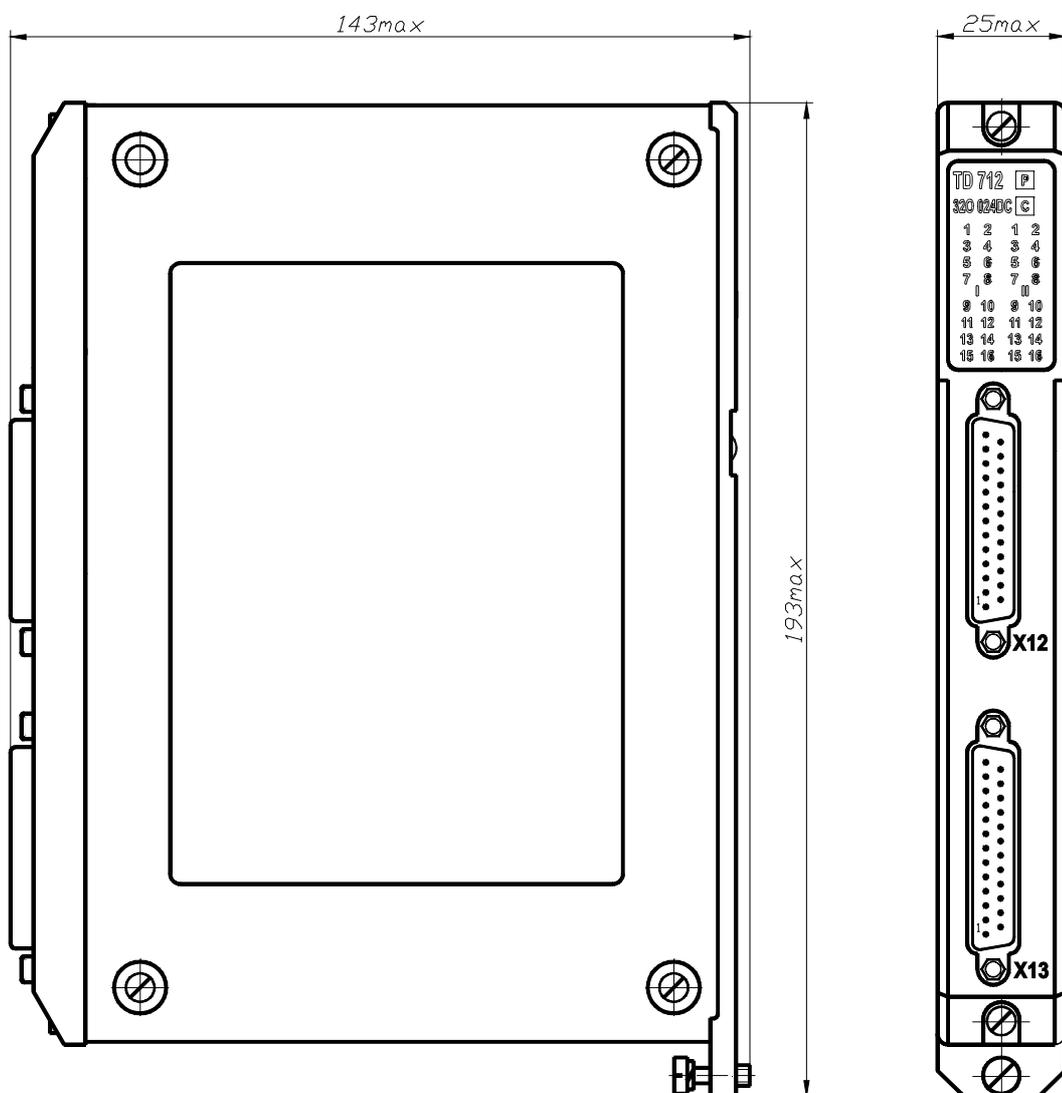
Внешний вид и габаритные размеры модуля TD 712
